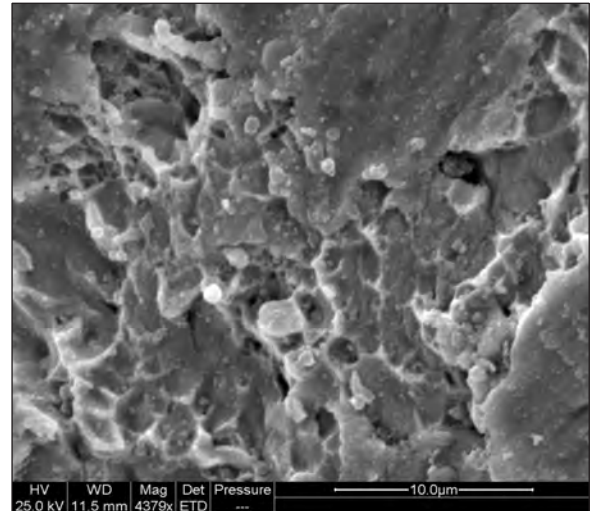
Wabenbruchstrukturen im Anschluss an den Schwingungsrissbereich
